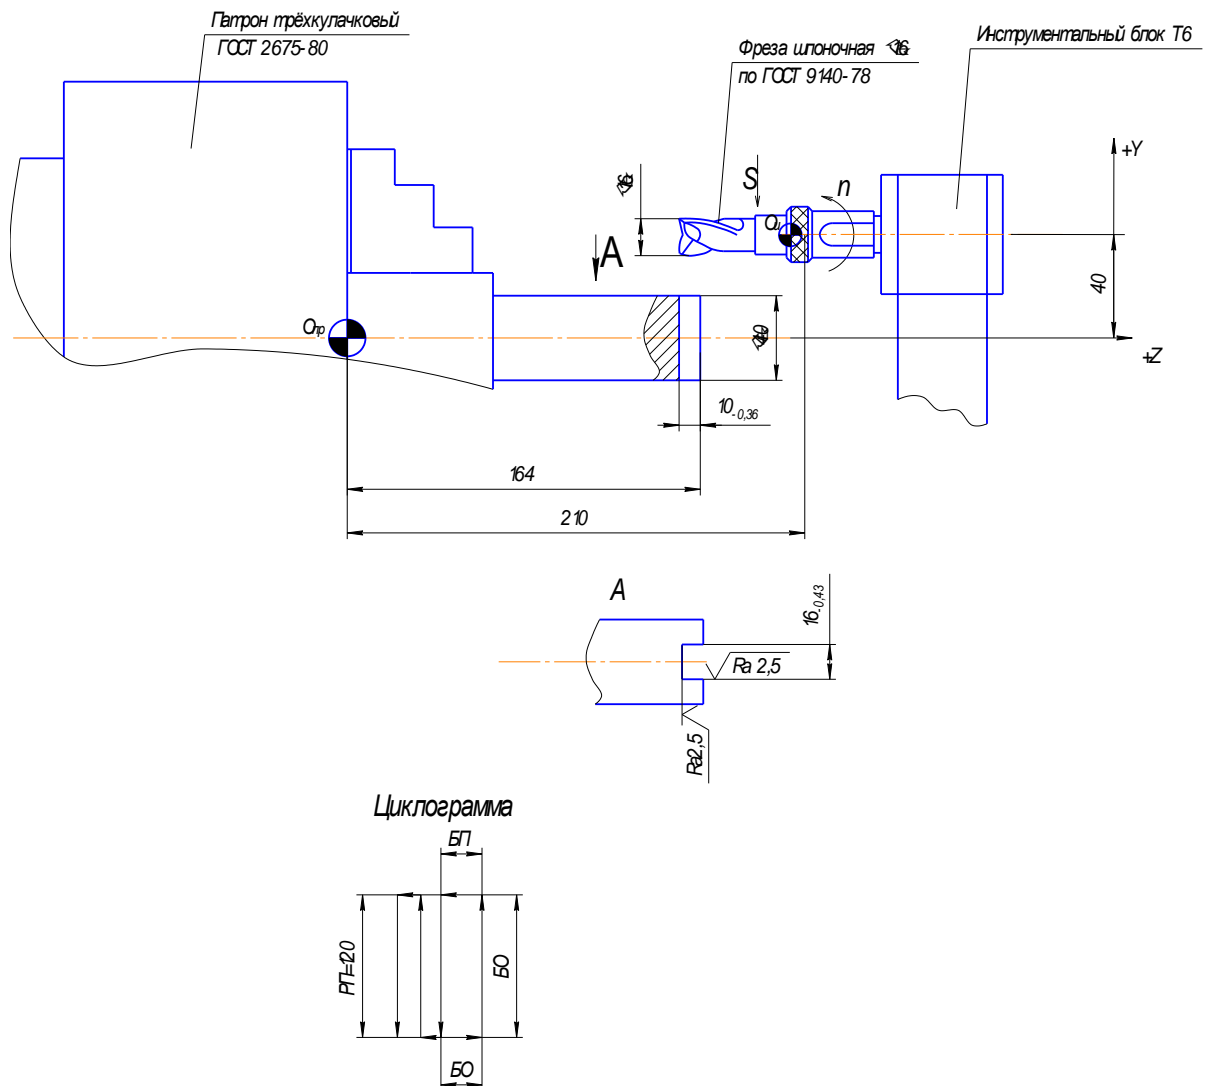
Схема наладки фрезерования поперечного шпоночного паза
